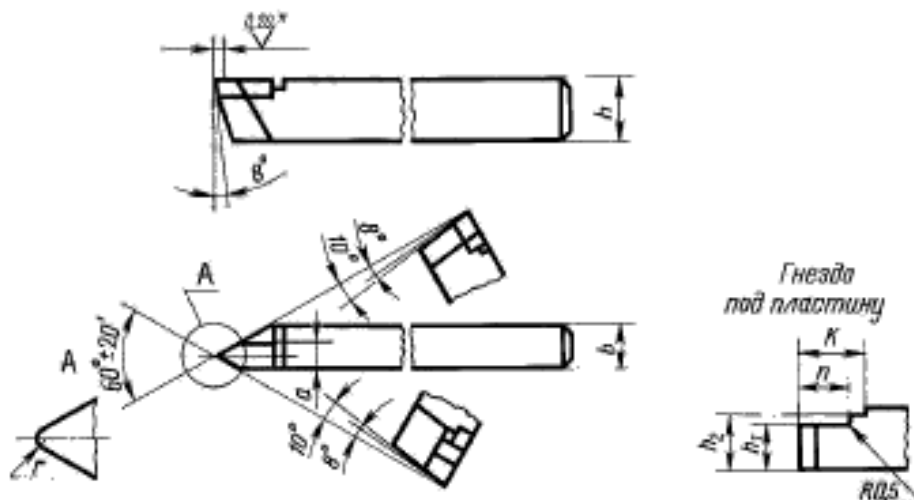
Робоче креслення різьбового різця згідно зі стандартом ДСТУ ГОСТ 18885-73
